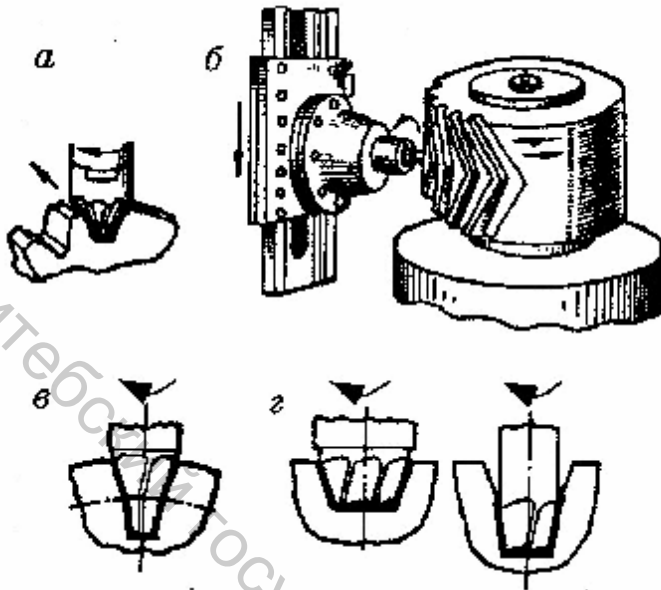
Нарезание зубьев зубчатых колес пальцевыми фрезами
